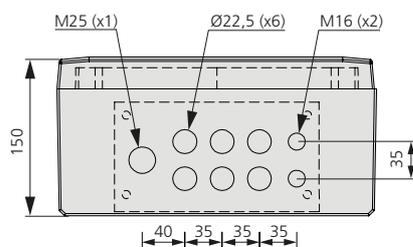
SuperWISE II, SuperWISE II SC parte inferior, esquema de dimensiones.
